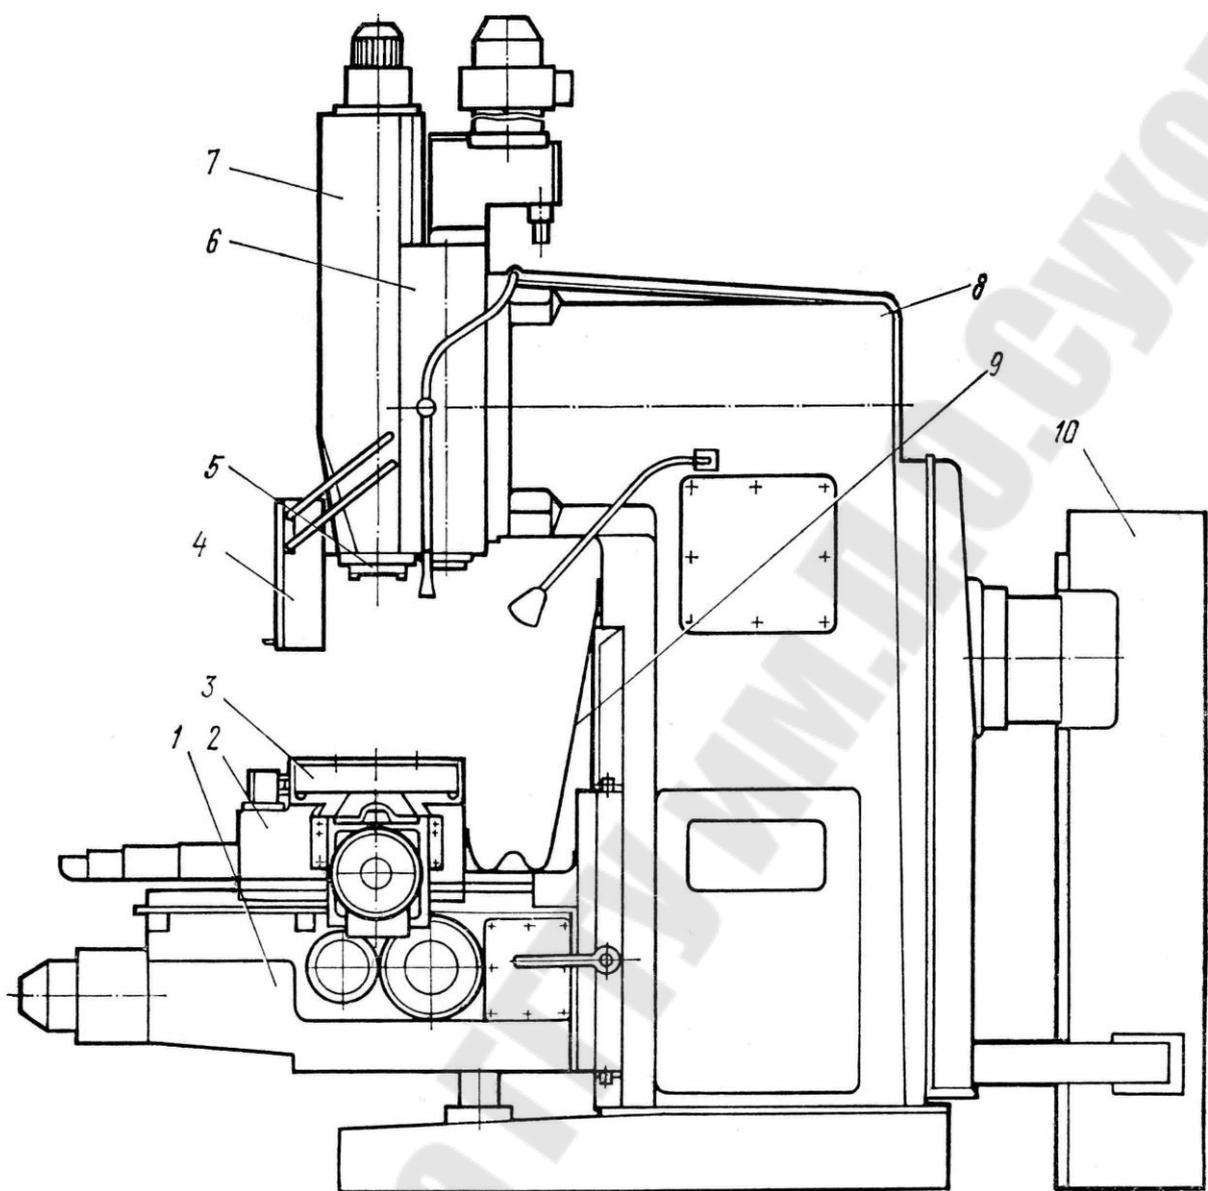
Общий вид вертикально-фрезерного станка с ЧПУ
